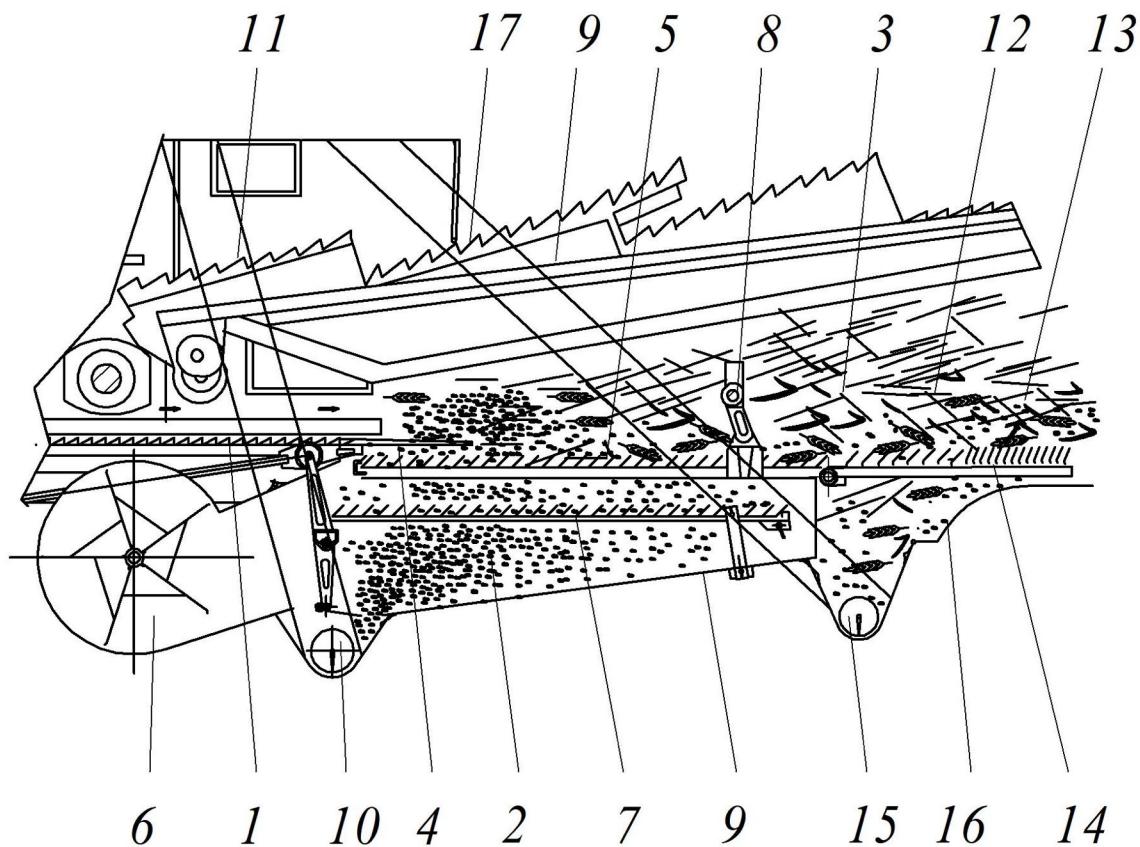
Воздушно-решётная очистка комбайна: 1 – транспортная доска; 2 – зерно; 3 – соломистые примеси, половы; 4 – пальцевая гребёнка; 5 – верхнее решето; 6 – центробежный вентилятор; 7 – нижнее решето; 8 – сайлент-блоки; 9 – наклонное днище; 10 – зерновой шнек; 11 – зерновой элеватор; 12 – необмолоченные колосья; 13 – свободное зерно; 14 – дополнительное решето или удлинитель грохота; 15 – колосовой шнек; 16 – скатная поверхность; 17 – колосовой элеватор.
